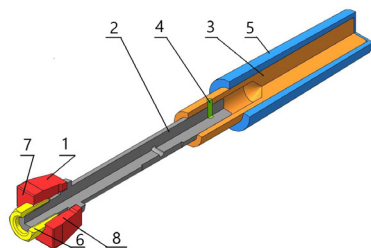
Дорн для электромеханической заправки отверстий квадратного сечения; 1 - упрочняющий зуб, 2 – оправка, 3- переходная втулка, 4 – штифт, 5 - токоизоляционная втулка, 6 – коническая гайка; 7 упругий сегмент, 8 – прорези между сегментами
